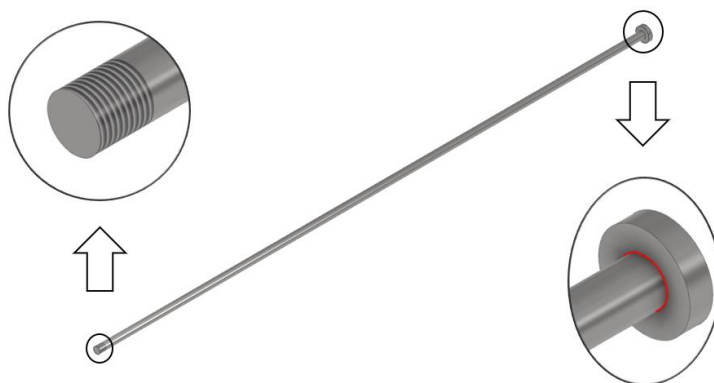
Roscagem e soldadura no pino da dobradiça do alçapão.
